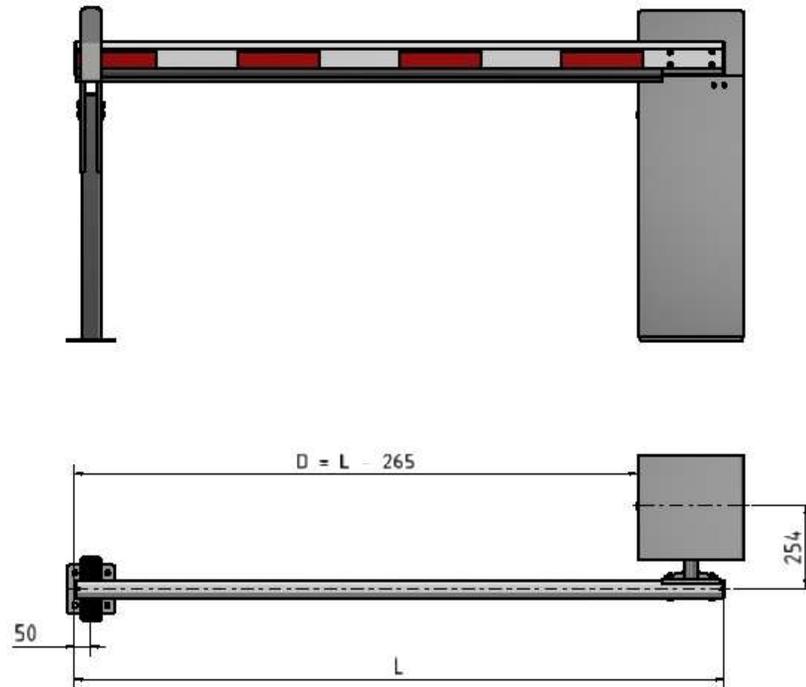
Plan d'installation boîtier de la barrière – montant : dimensions en mm
